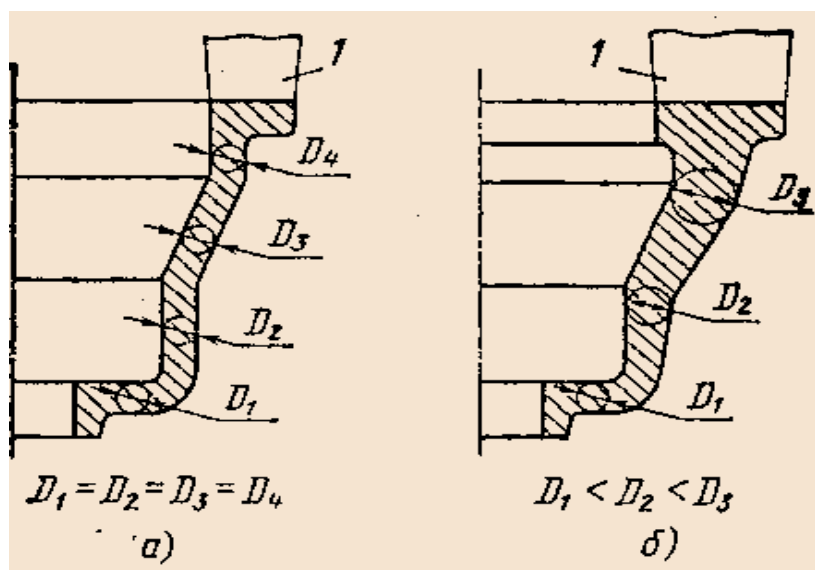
38. Конструкции литых деталей, обеспечивающих одновременное (а) и направленное затвердевание (б) отливок: 1 – прибыль
